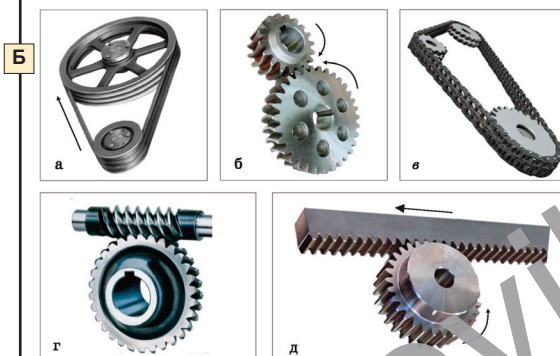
Передаточные механизмы: а – ременная передача; б – зубная передача; в – цепная передача; г – винтовая передача; д – зубчато-реечная передача
